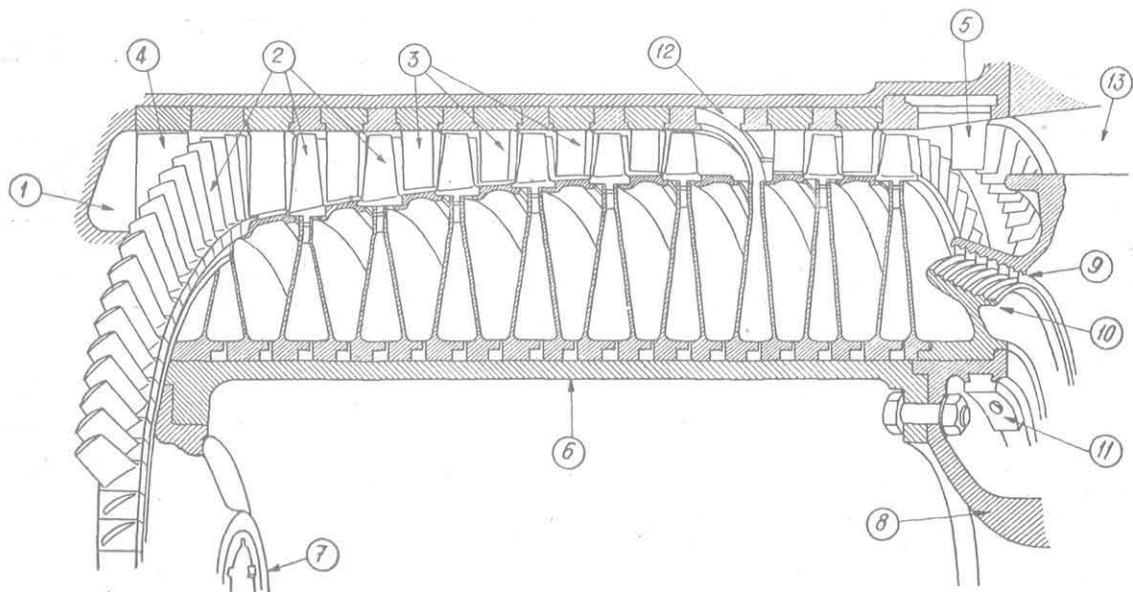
Corte esquemático del compresor de la turbohélice Mamba: (1), entrada de aire; (2), álabes del rotor; (3), álabes del estator; (4), álabes-guías de entrada; (5), álabes-guías de salida; (6), tambor o cilindro-soporte; (7), acoplamiento del eje de la hélice; (8), acoplamiento del eje de la turbina; (9), cierre de laberinto; (10), igualador del empuje axial; (11), pesos para el equilibrado dinámico. (12), alojamiento de los álabes; (13), salida del aire.
